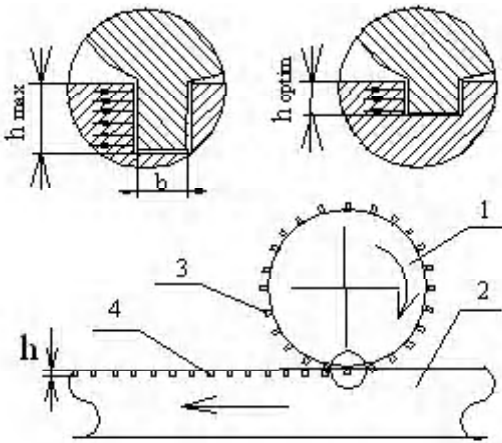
Схема взаимодействия валка и заготовки в процессе непрерывного литья:
